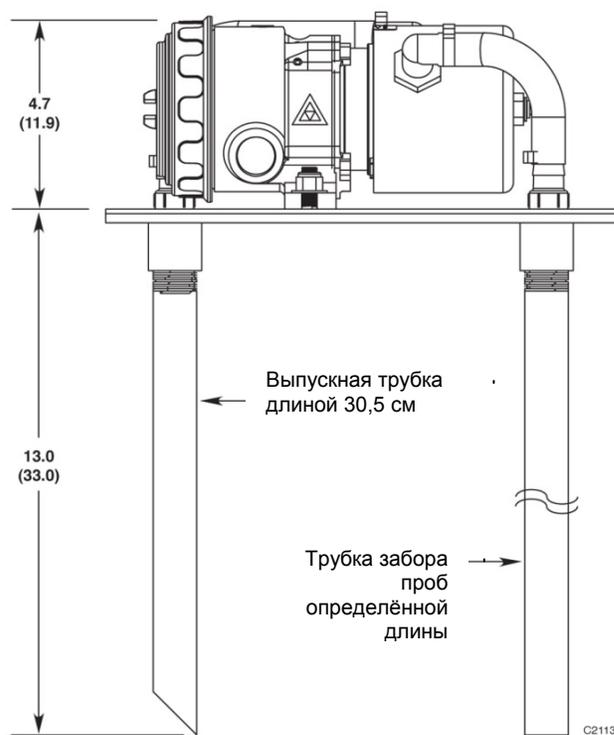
Габаритные размеры газоанализатора и набора Q900 в сборе, в дюймах (см).
